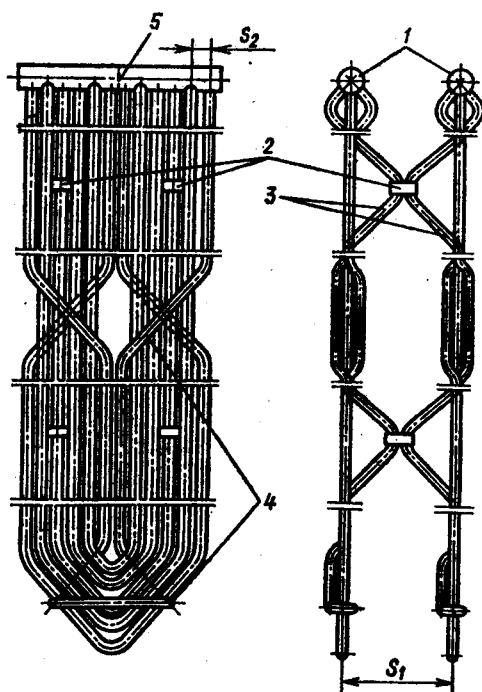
Ширмовый пароперегреватель: 1 — коллектор; 2 — соединительный элемент; 3 — трубы ширмового пароперегревателя; 4 — трубы обвязки; 5 — разделительная перегородка
